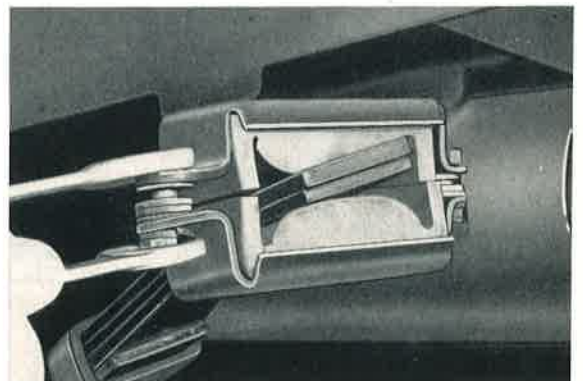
/3: Zum Ausbau einer Hinterfeder wird die Auflage f. Gummiblock vorn abgeschraubt, hinten gelockert.
